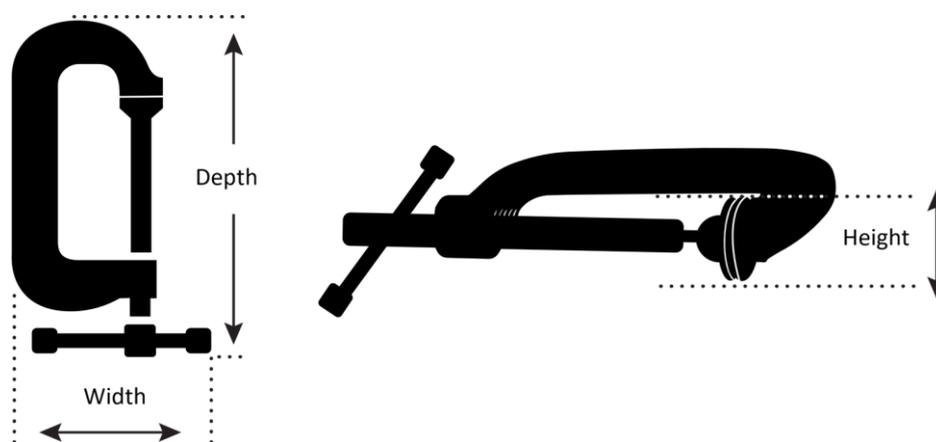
81/82: Abmessungen von unverpackten Handwerkzeugen
